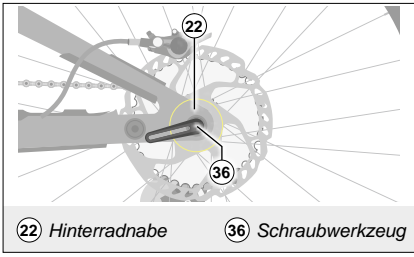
Schraubwerkzeug für Akku an Hinterradachse
